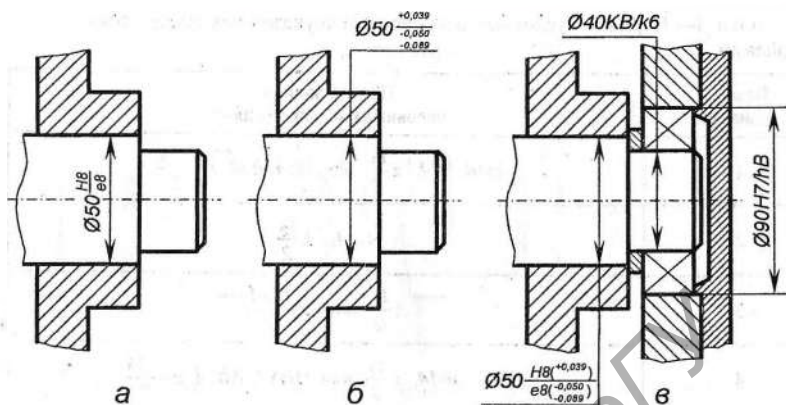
Примеры обозначения посадок на сборочных чертежах
